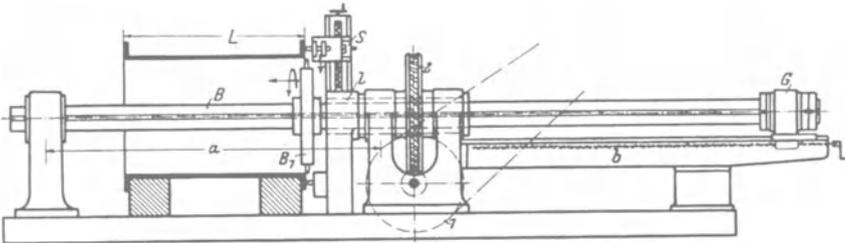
Zylinderbohrwerk mit wandernder Bohrstange.
